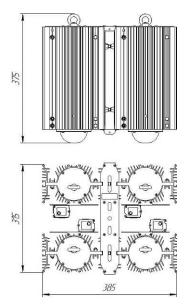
Габаритный чертеж светильника Econex Hell (480 70°C /240 100°C)
